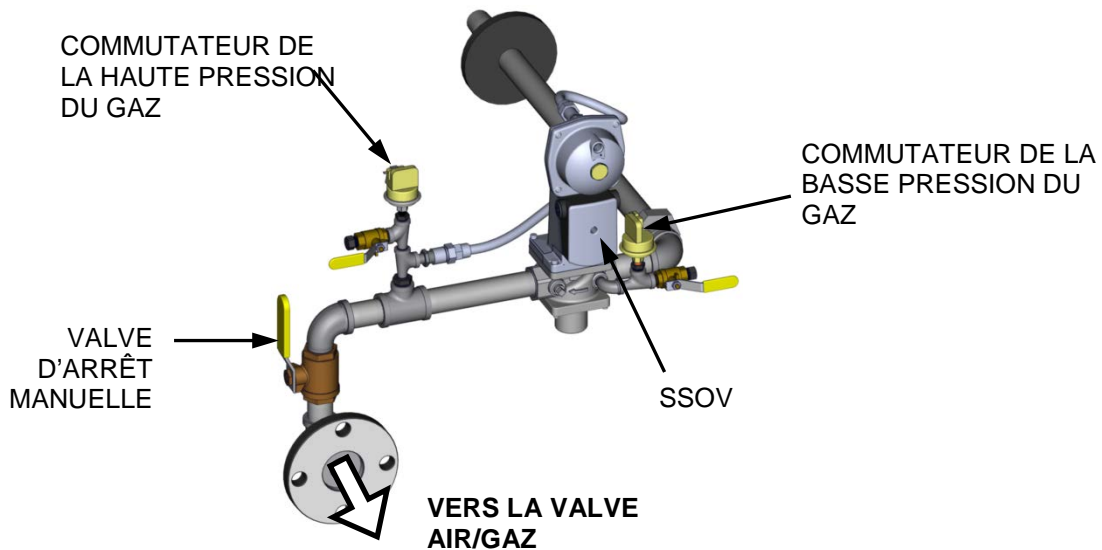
Emplacement de la valve d'arrêt manuel du gaz (circuit de gaz INN1060)
